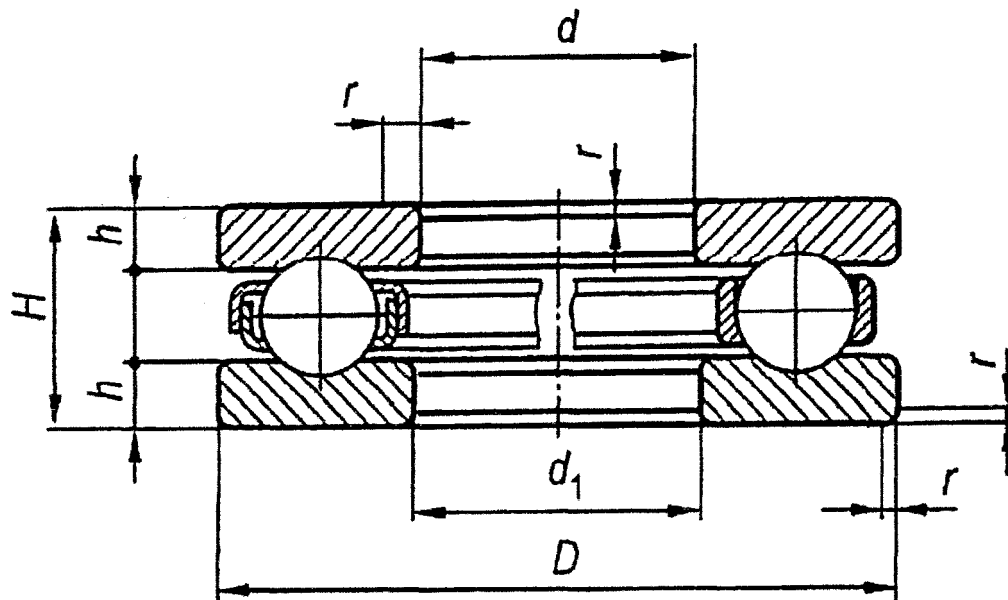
Подшипник шариковый упорный одинарный исполнения 8000H ($d_1 \geq d + 2$)
